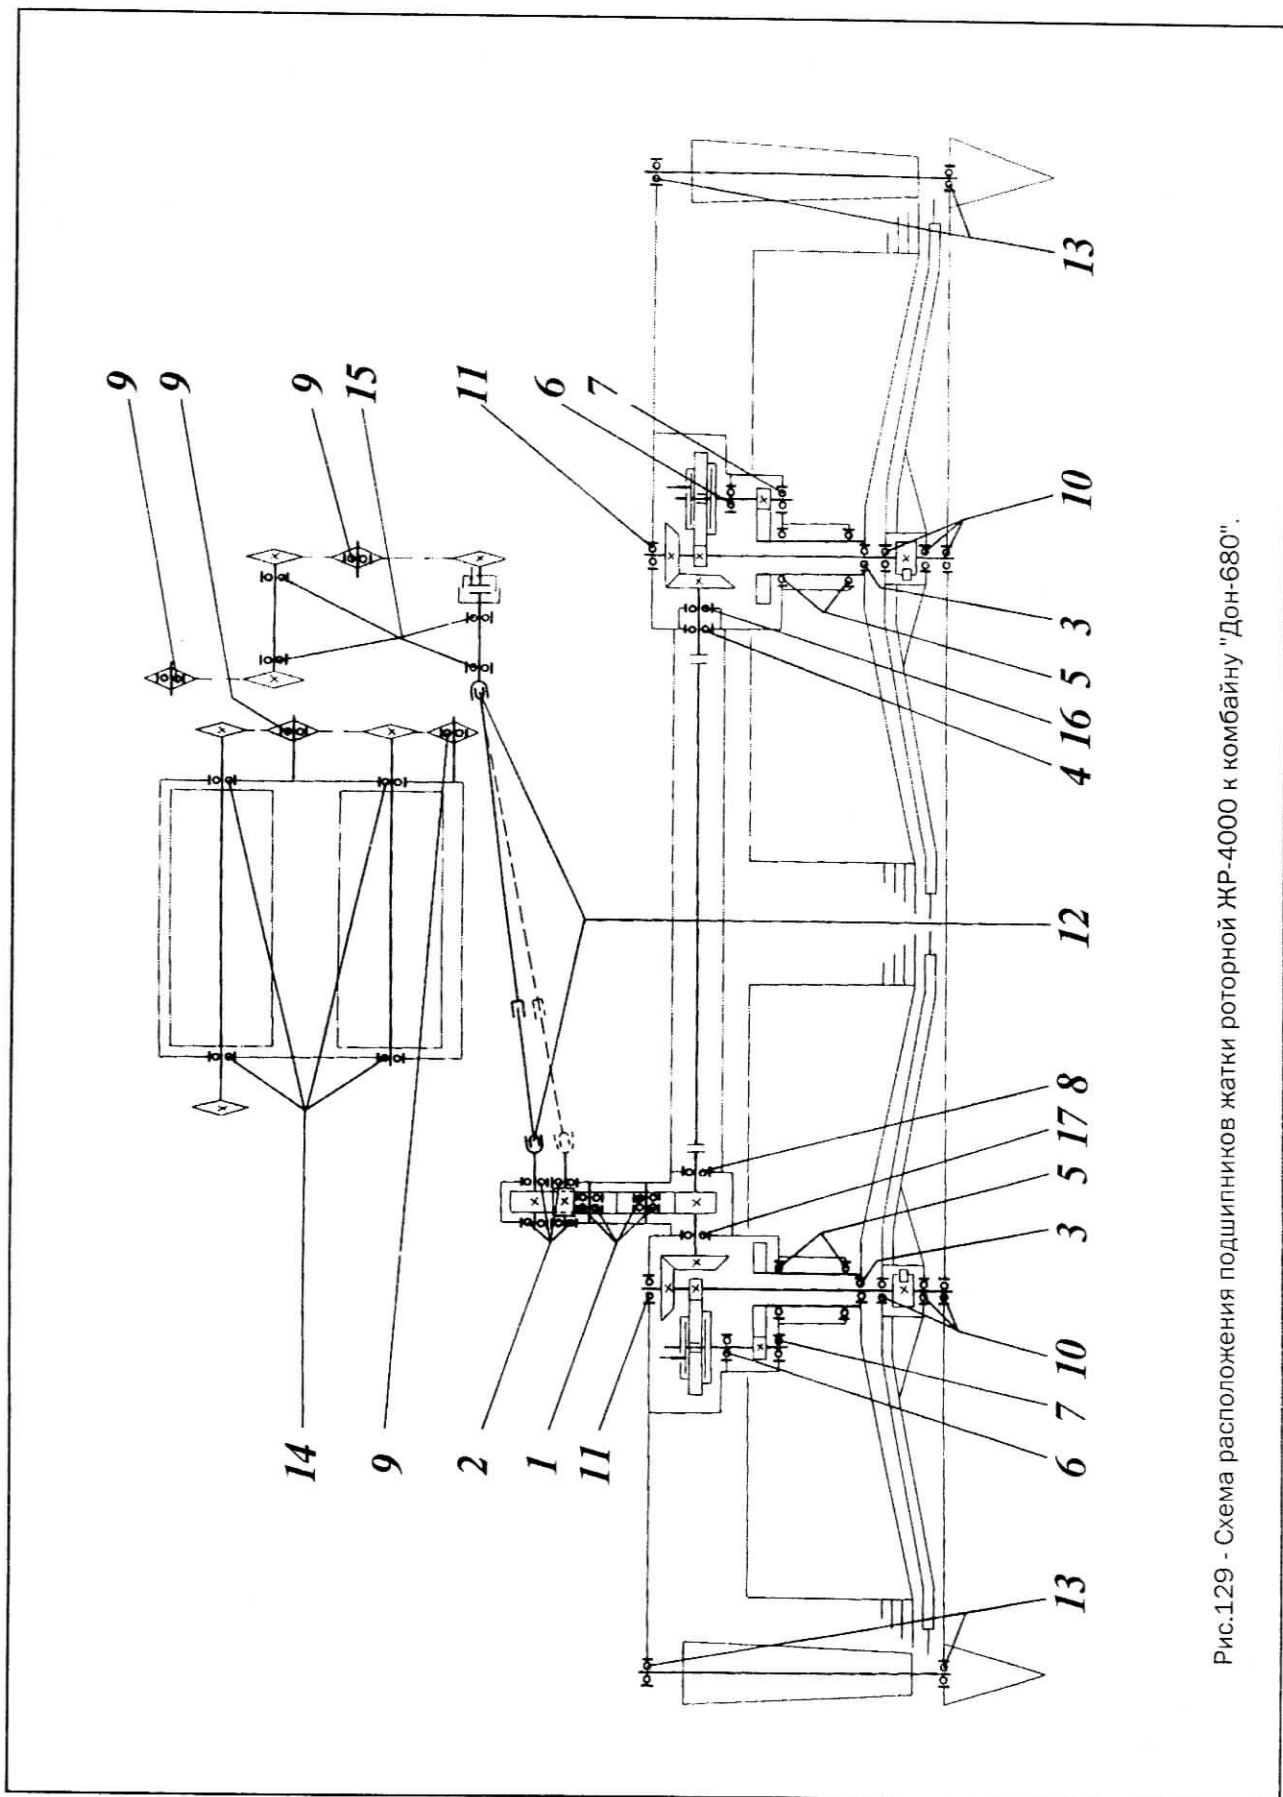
Схема расположения подшипников жатки роторной ЖР-4000 к комбайну "Дон-680".
